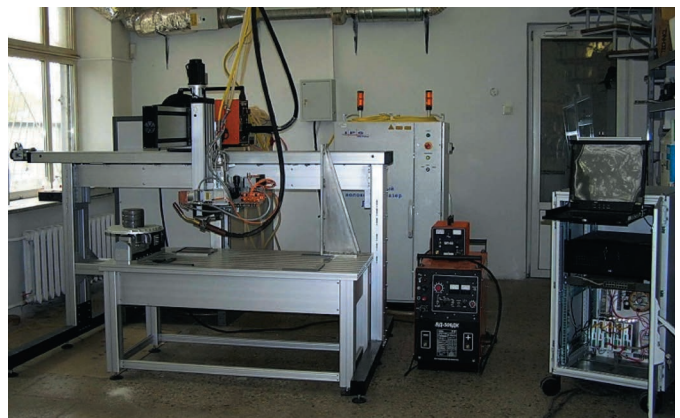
Портальная машина для сварки объемных легких конструкций.
